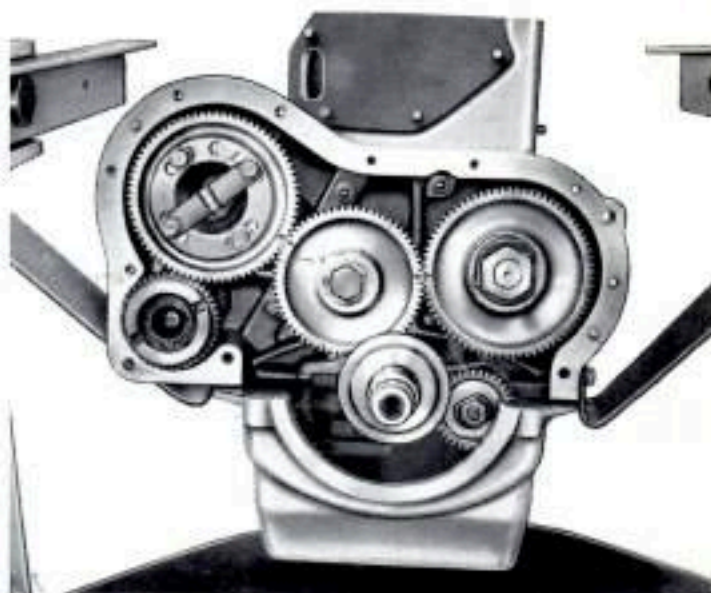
Smontaggio del motore: è stato tolto il coperchio ingranaggi distribuzione.
